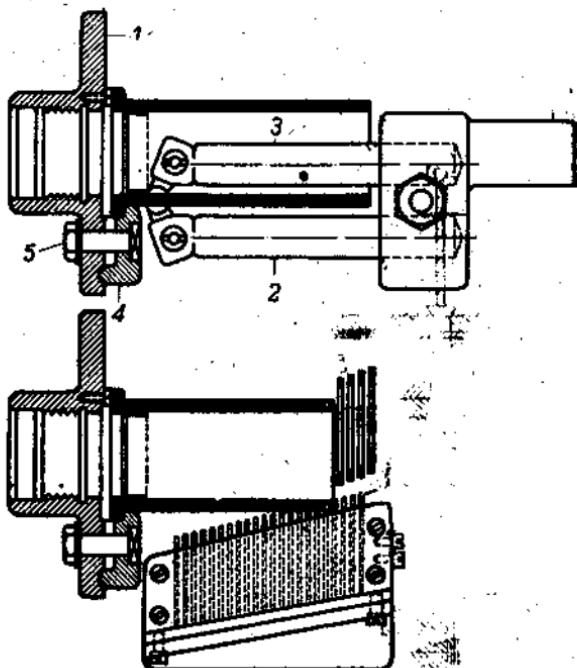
Приспособление для отрезания от заготовки поршневых колец.
